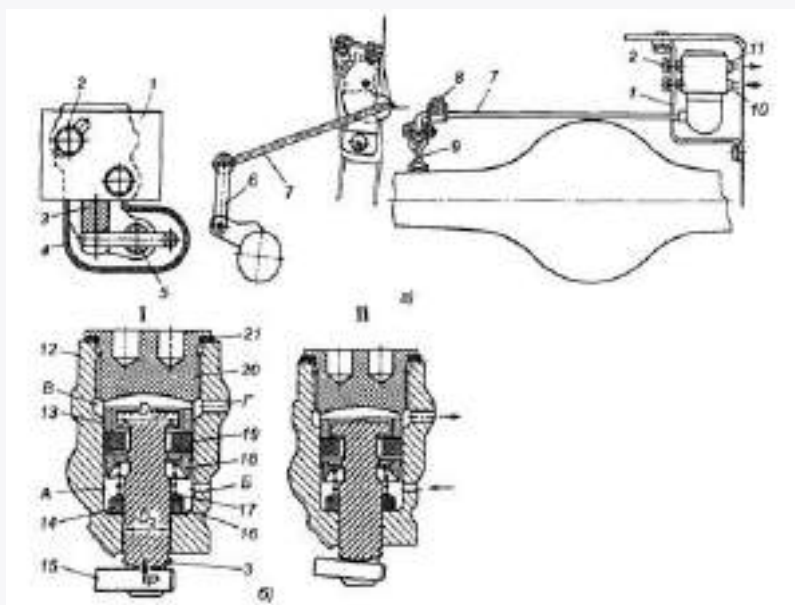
Регулятор давления жидкости в тормозных механизмах задних колес автомобилей марки «ВАЗ» семейства «Жигули»: а — расположение регулятора на автомобиле; б — схема работы; 1 — поршень-клапан открыт; 2 — поршень-клапан закрыт; 1 — кронштейн; 2 — болт крепления регулятора к кронштейну кузова; 3 — поршень-клапан; 4 — корпус регулятора; 5 — палец; 6 — тяга; 7 и 15 — торсионные рычаги; 8 — скоба; 9 — вилка; 10 — штуцер трубопровода, подводящего жидкость из главного цилиндра; 11 — штуцер трубопровода, отводящего жидкость из регулятора к колесным цилиндрам; 12 — корпус; 13 — распорное кольцо; 14 — уплотнительное кольцо; 16 — гнездо уплотнительного кольца; 17 — пружина поршня; 18 — упорное кольцо; 19 — уплотнительное кольцо клапана; 20 — пробка; 21 — прокладка; А и В — полости; Б — отверстие для штуцера трубопровода от главного цилиндра; Г — отверстие для штуцера трубопровода к тормозным механизмам задних колес; Р — сила, действующая на поршень от торсионного рычага при уменьшении расстояния от кузова до заднего моста.
